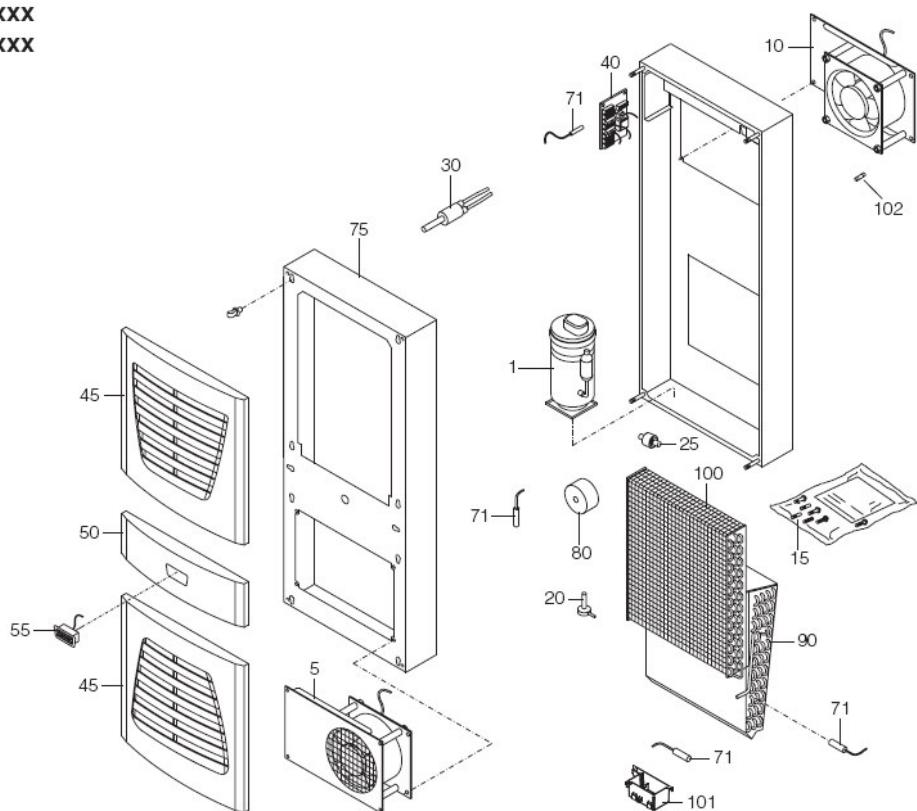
SK 3304.xxx 型和SK 3305.xxx 型的备件
